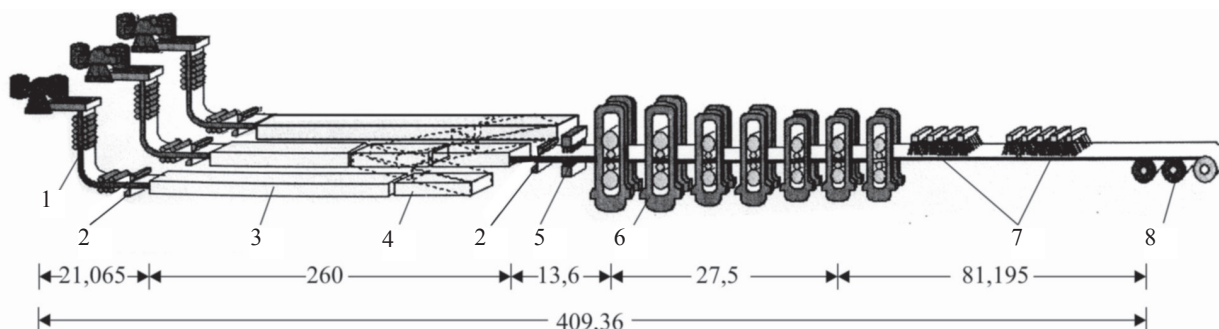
Схема расположения оборудования трёхручьевого тонкослябового литейно-прокатного агрегата: 1 – МНЛЗ; 2 – ножницы поперечной резки; 3 – проходная роликовая печь; 4 – передаточное устройство; 5 – гидросбив окалины; 6 – непрерывная группа клетей; 7 – ламинарная душирующая установка; 8 – моталки
